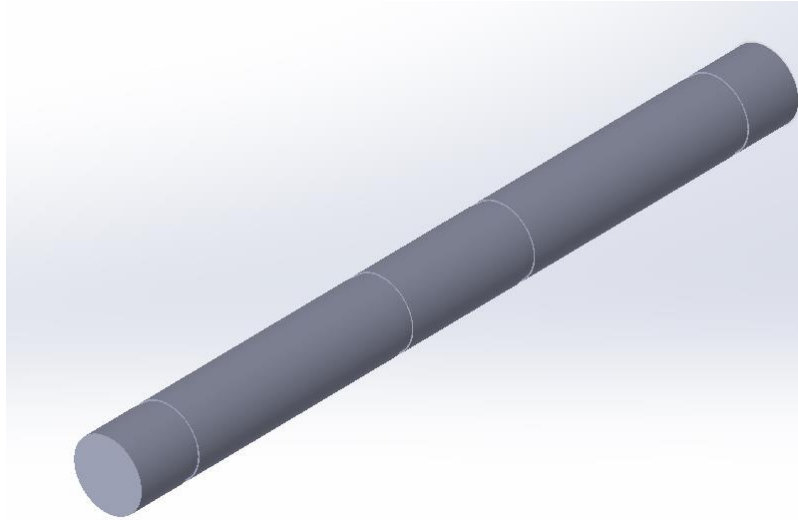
Vista de pieza eje 12 (Fuente 110)
